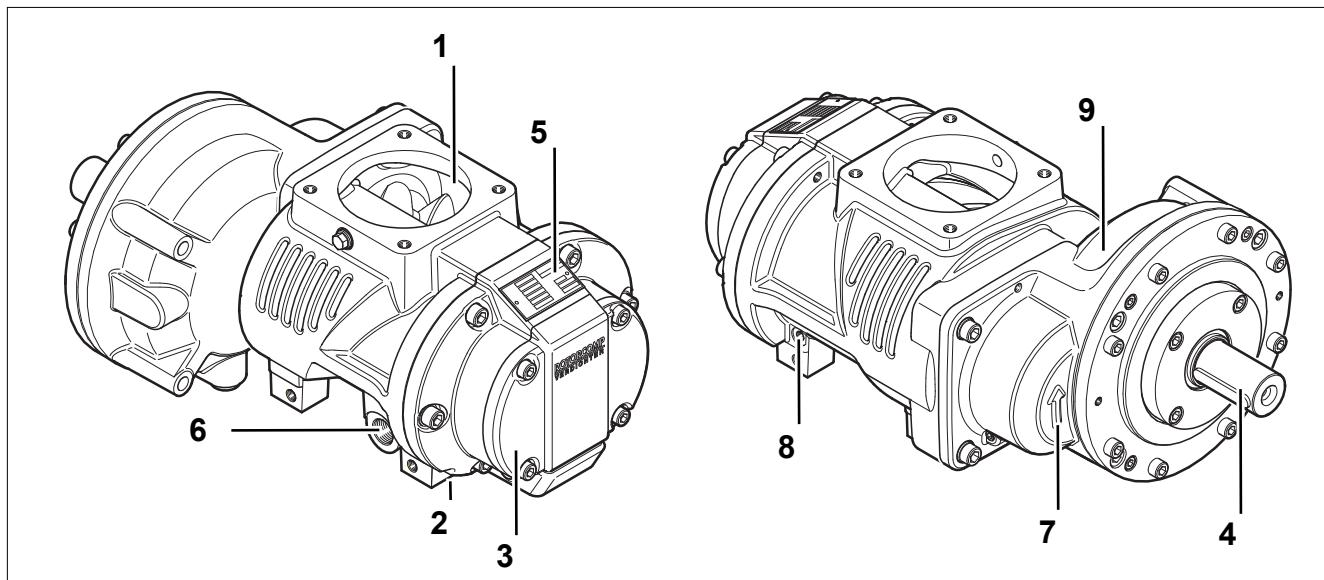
Винтовой блок EVO 9 GH (горизонтальный редуктор)
